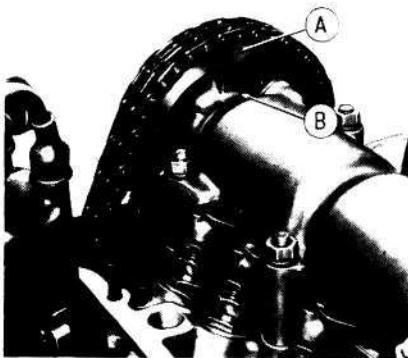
Установка поршня четвертого цилиндра в ВМТ
